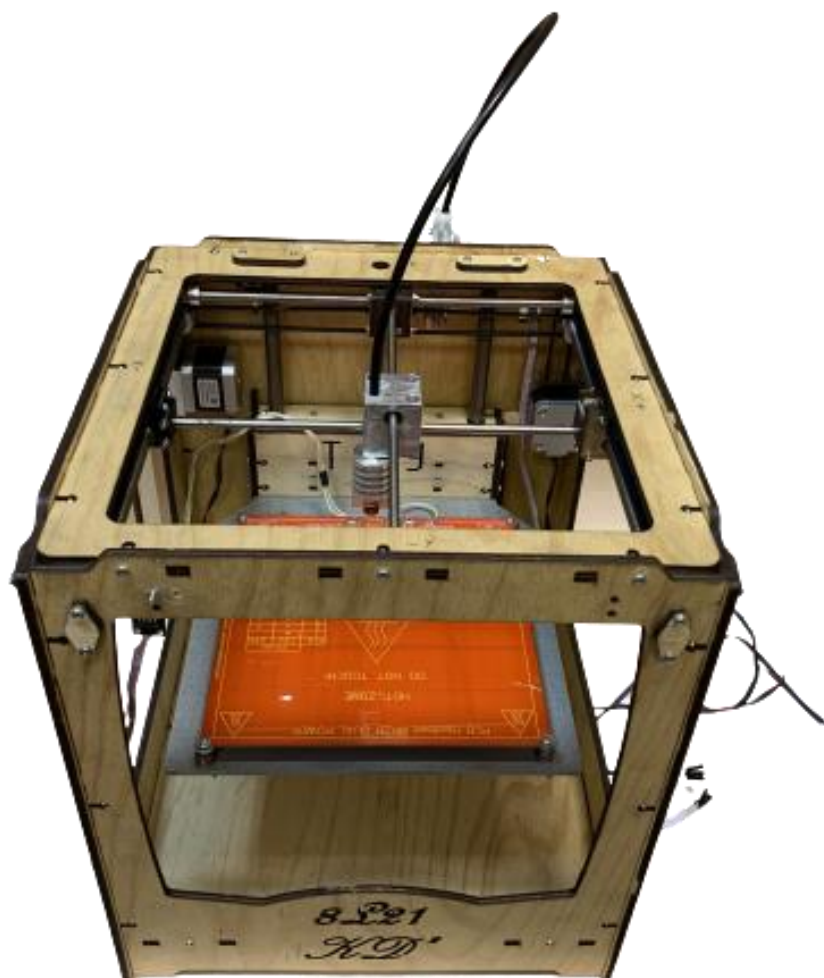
Сборка механической части 3D-принтера
